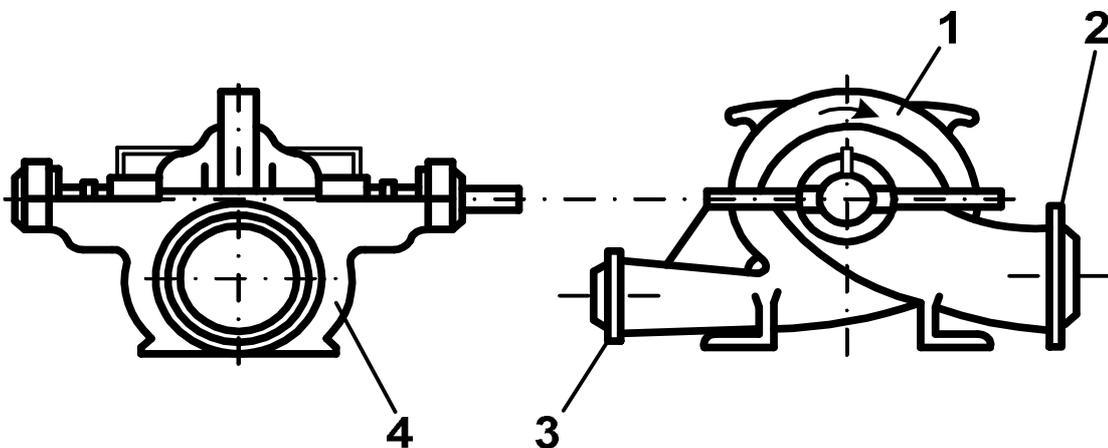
Корпус насоса типа Д: 1 – крышка; 2 и 3 – всасывающий и нагнетательный патрубки; 4 – корпус (постель)
